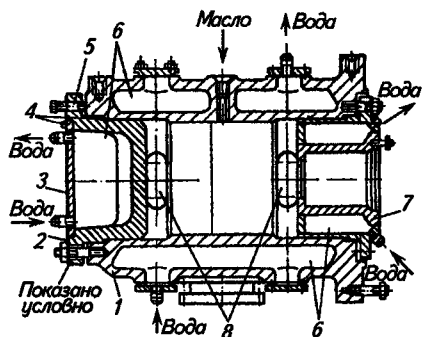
Цилиндр компрессора АО-600 в сборе:
